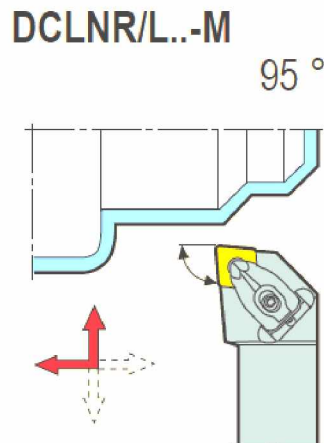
Різець для зовнішньої обробки з ромбічною пластиною
